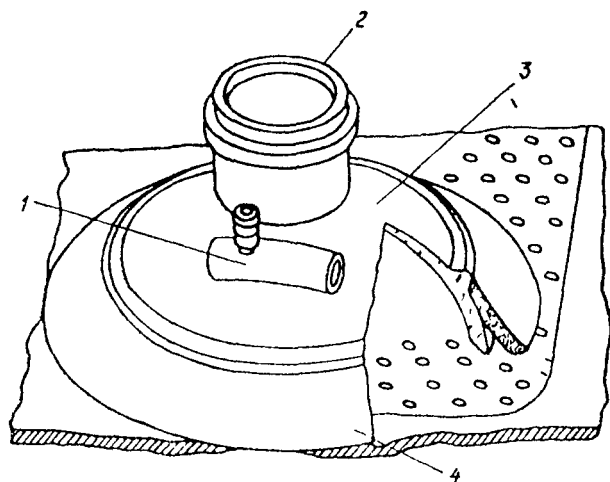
Схема местной проверки на герметичность: 1 — эжекторный насос; 2 — вакуумметр; 3 — колпачок из органического стекла; 4 — окантовка из губчатой резины
